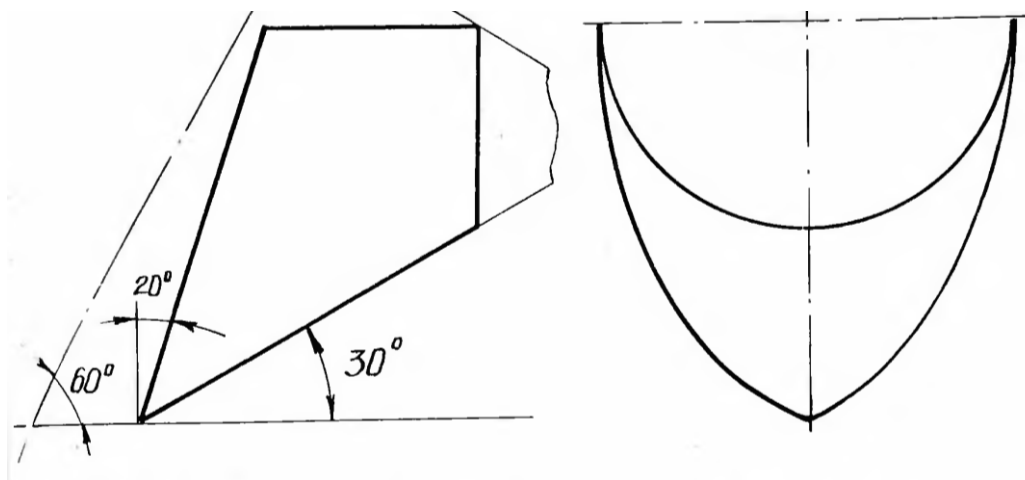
Робочий орган совкового типу з конічною поверхнею підйому для грейдера Д-437А
